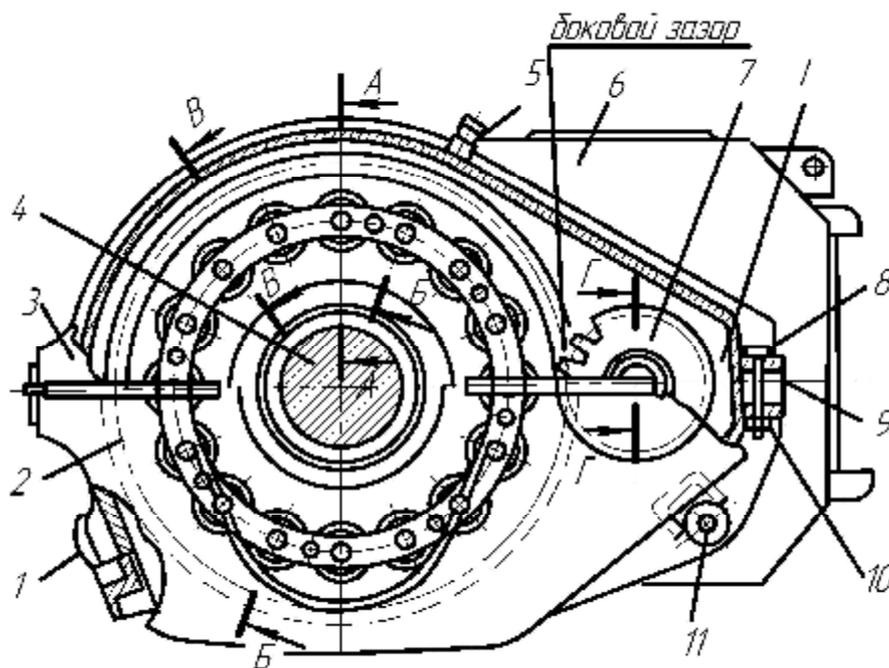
Измерение бокового зазора в зубьях тягового редуктора: 1 – пробка заливной горловины; 2, 3 – половина кожуха нижняя и верхняя; 4 – ось колесной пары; 5 – сапун; 6 – тяговый электродвигатель; 7 – шестерня ведущая; 8, 11, 22 – болты; 9 – прокладка; 10 – гайка
